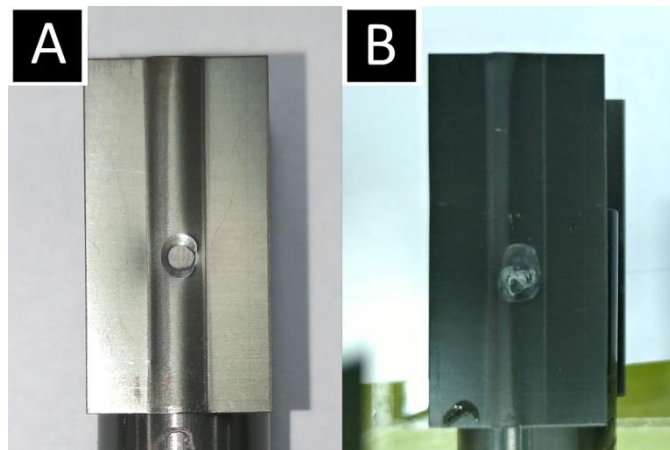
Lentilha de Solda Máxima: A – Superfície do corpo de prova sem corrosão; B – Superfície do corpo de prova com corrosão.
